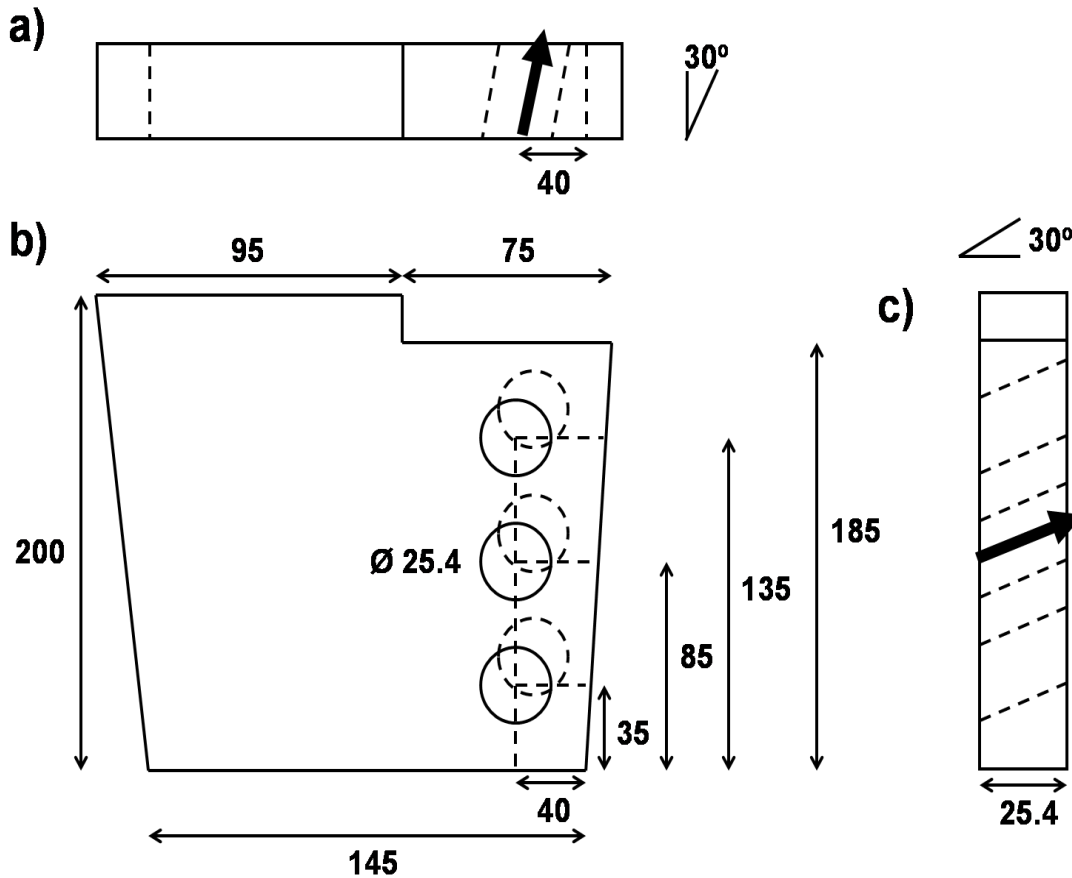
Geometría y dimensiones de los baffles (mm): a) Vista superior, b) Vista frontal, c) Vista lateral.
